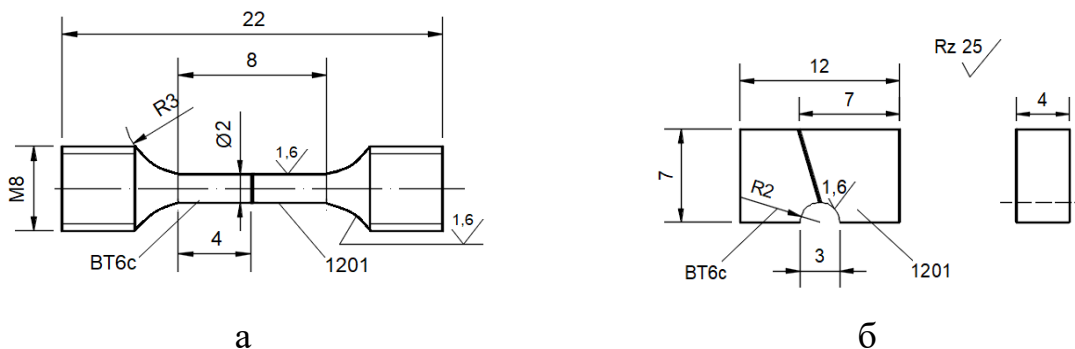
Форма и размеры образцов для испытаний:
